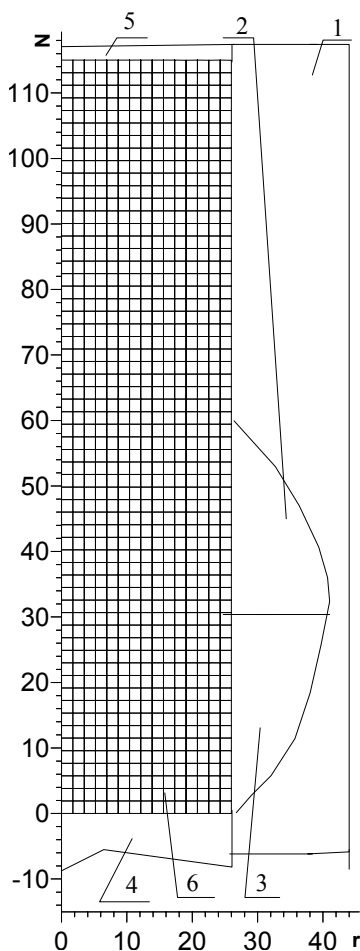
Розрахункова схема для осаджування (вихідний стан)
